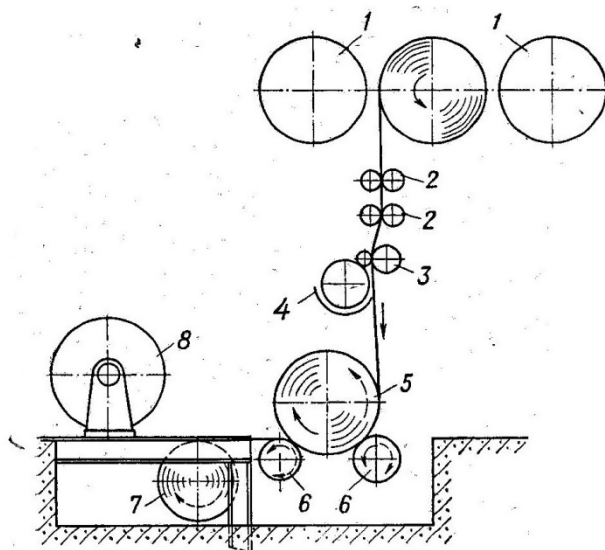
Принципиальная схема рулоноупаковочного агрегата:
